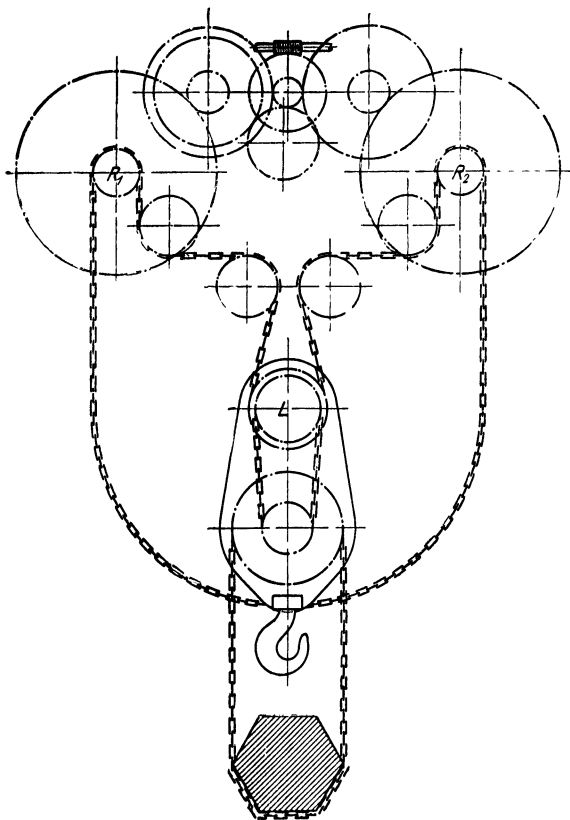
Schema einer Wendevorrichtung für Schmiedestücke.
